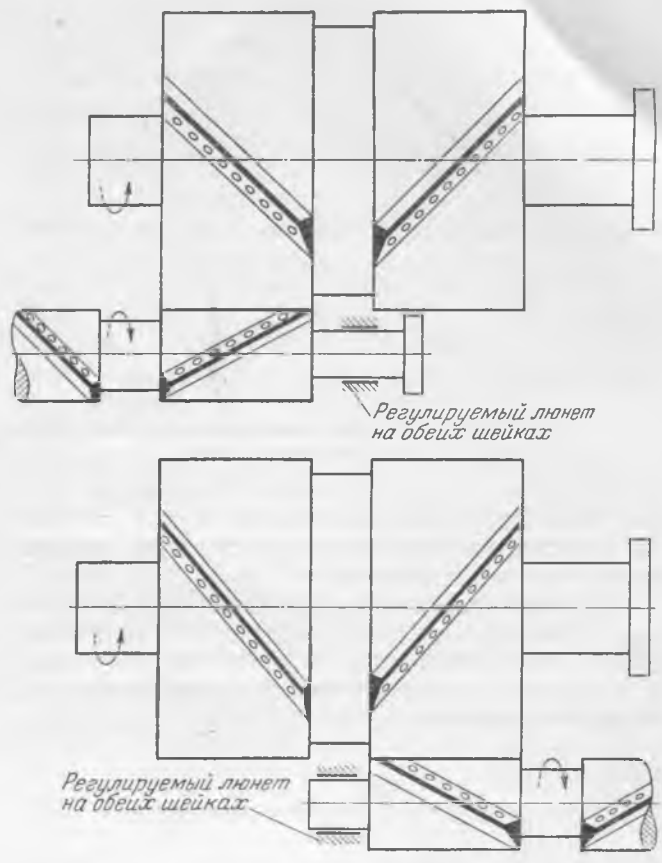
Схема установки шестерни для исправления профиля зубьев колеса по нерабочим сторонам зубьев шестерни.
